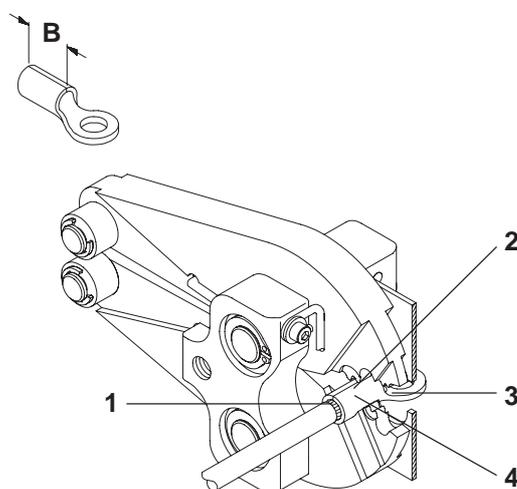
Crimpen einer STRATO-THERM-Anschlussklemme
